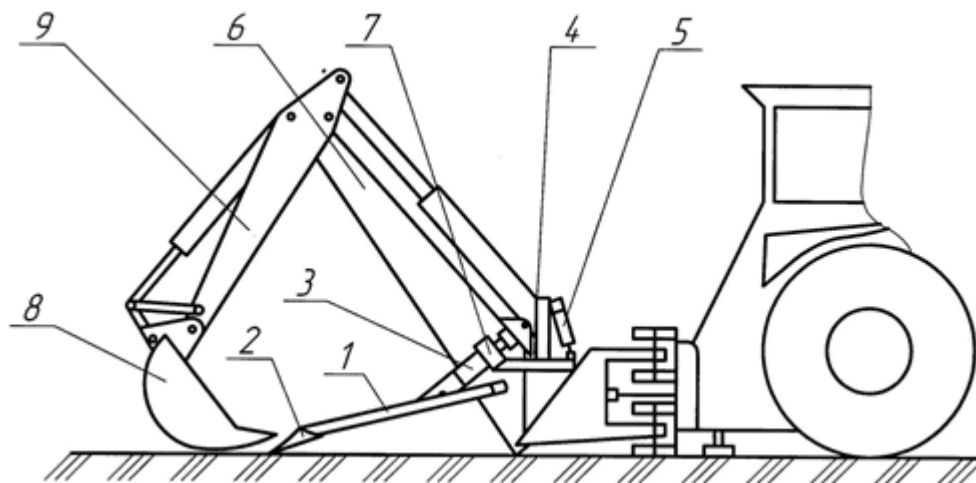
Очиститель ковша оборудования обратной лопаты:
